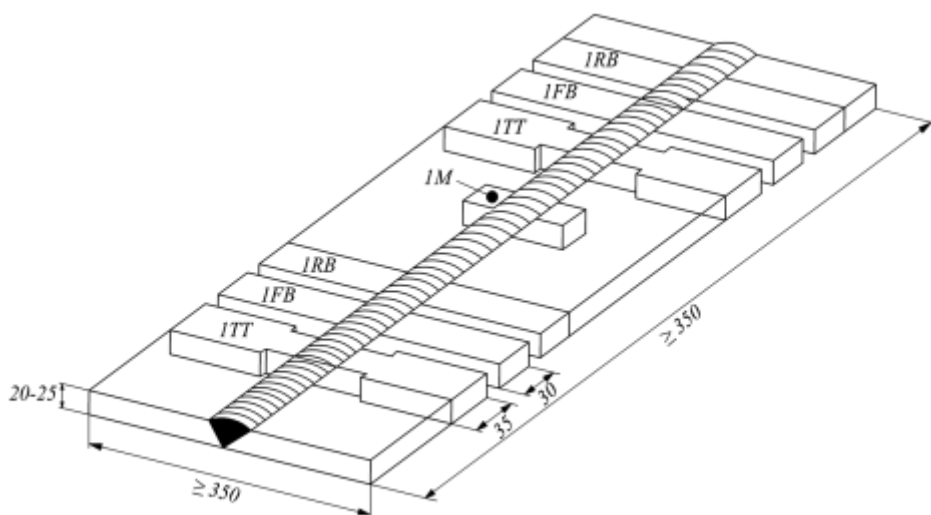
Додаткова проба стикового з'єднання для зварювання в нижньому просторовому положенні:
